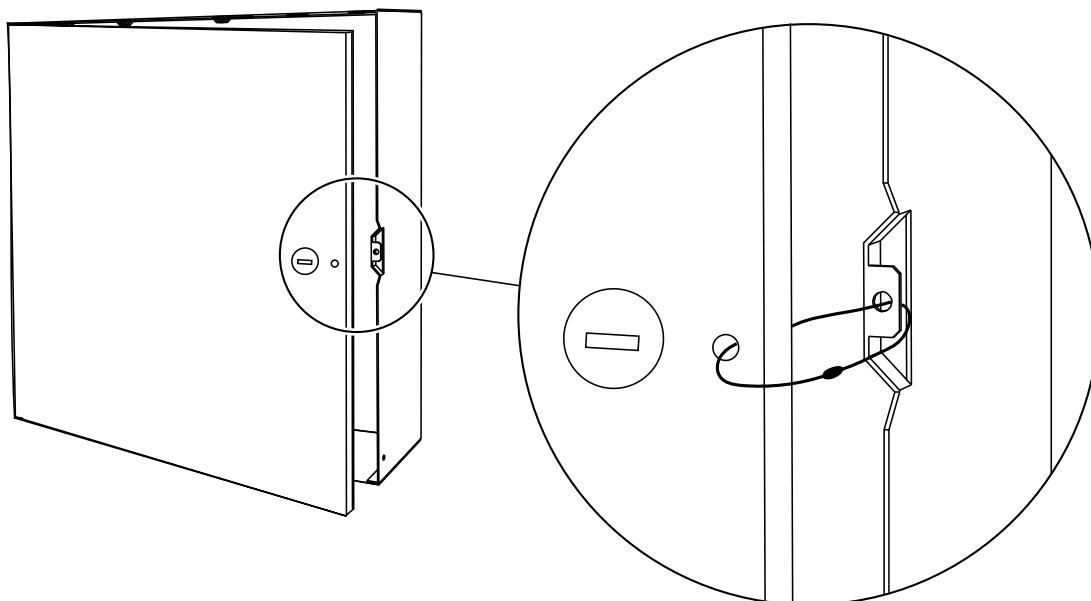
Selar a caixa com um fio de soldadura
